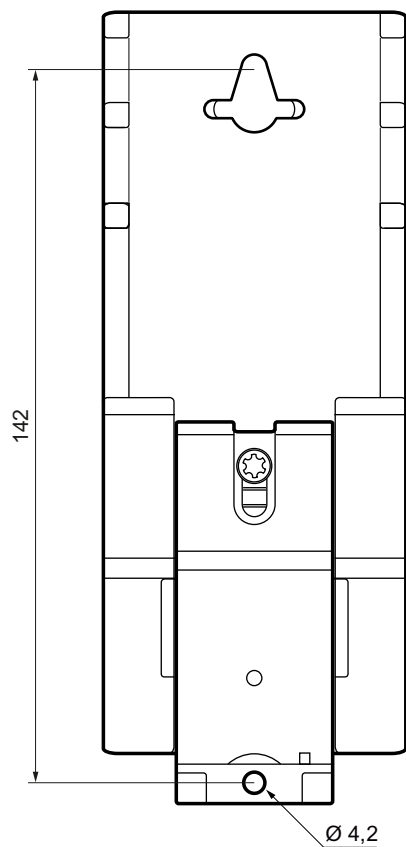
Bohrbild mit dem Befestigungsriegel in der Wandmontageposition (Lieferzustand)
